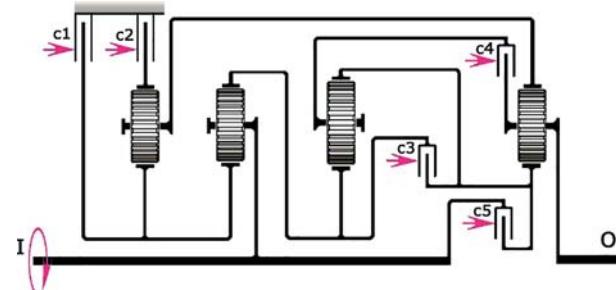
Кинематическая схема 8-ми ступенчатой планетарной коробки передач фирмы ZF Friedrichshafen:
